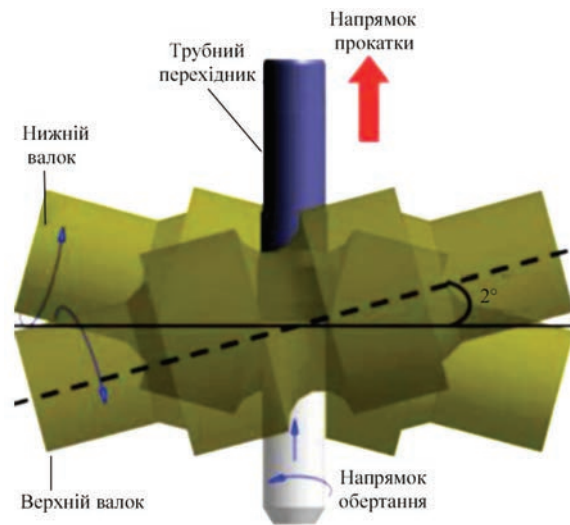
Зовнішній вигляд розміщення валків та напрямки руху під час прокатки (вид зверху)
